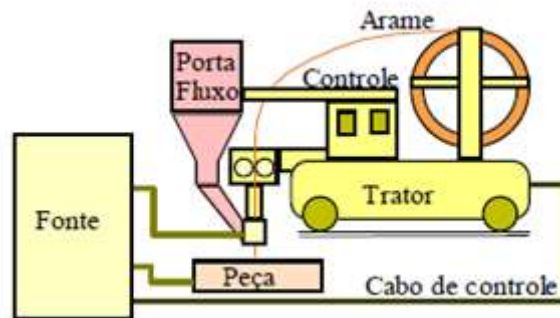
Equipamentos para a soldagem SAW – Fonte: Trabalho prático UFMG – Técnica operatória de soldagem SAW
